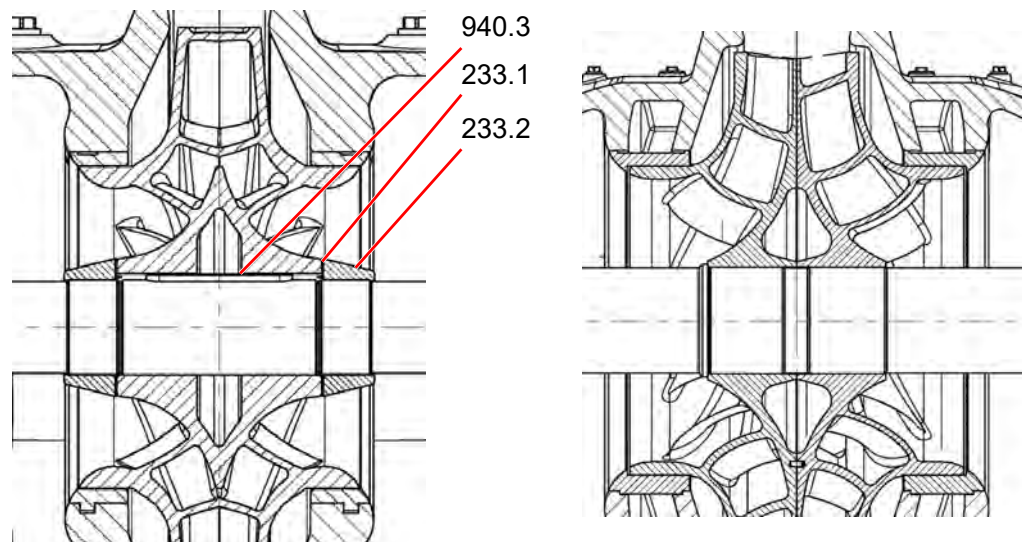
Крепление рабочего колеса при помощи призматической шпонки и гайки вала (слева) и прессовой посадки (справа)
